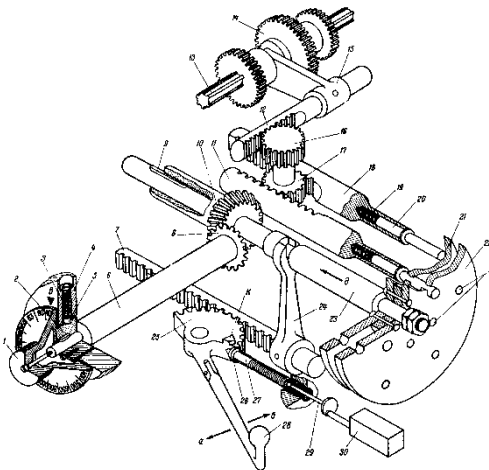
Схема механізму керування коробкою швидкостей
